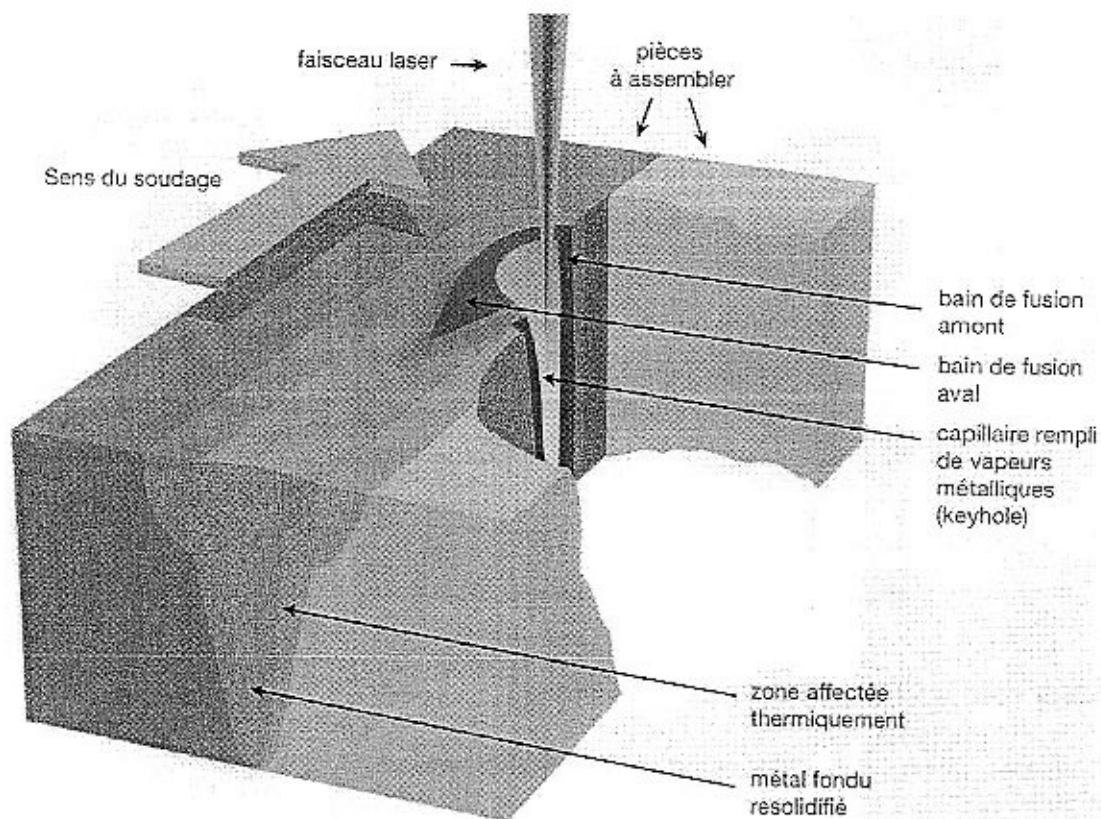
Principe d'une opération de soudage sous faisceau laser.
